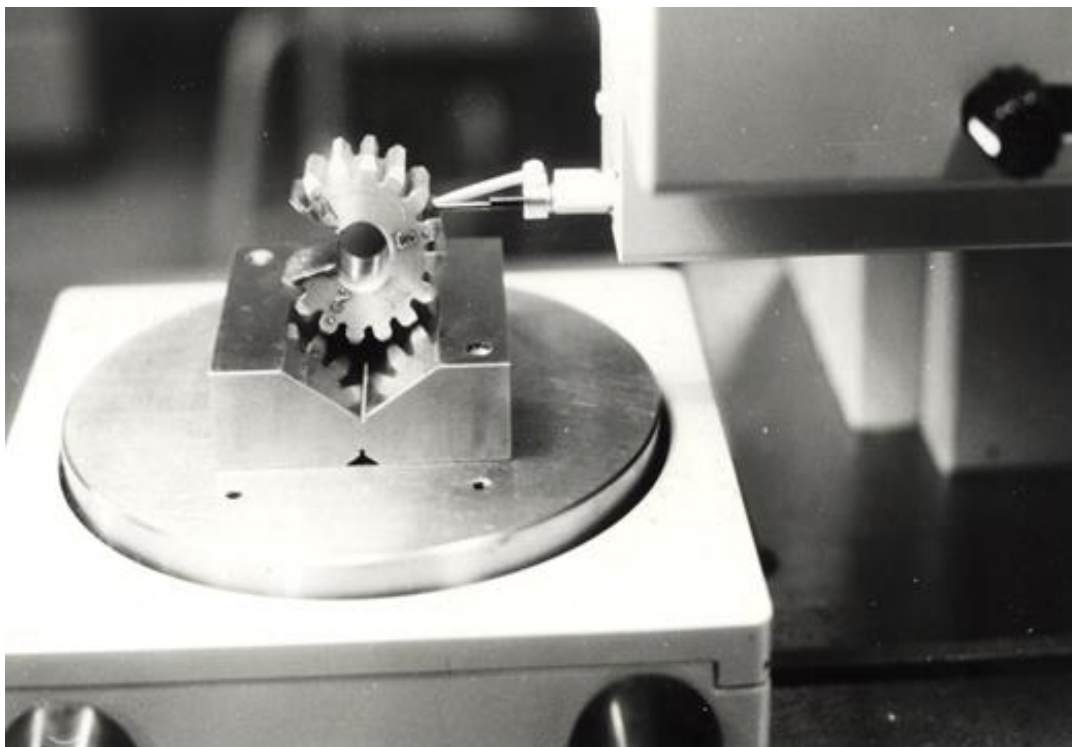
Измерение высоты шероховатости зуба зубчатого колеса
